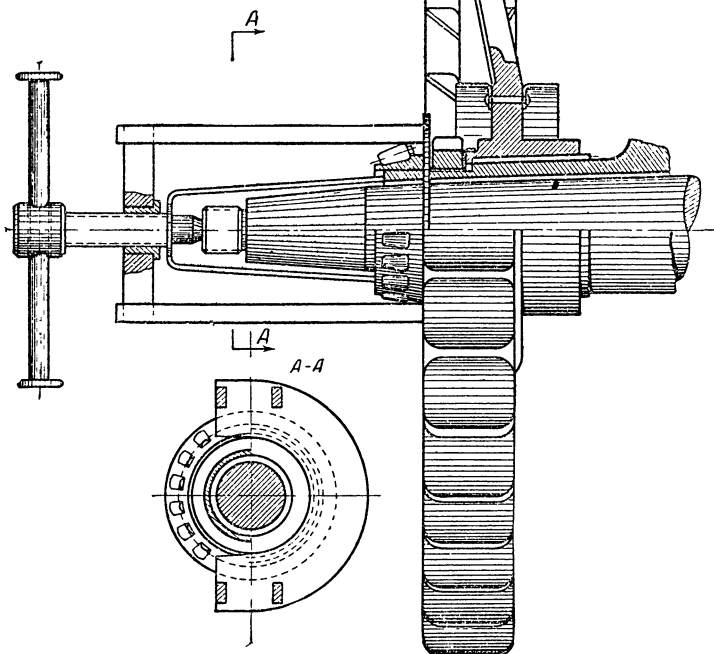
Съёмник для снятия наружного конического роликоподшипника бортового редуктора со ступицы.
